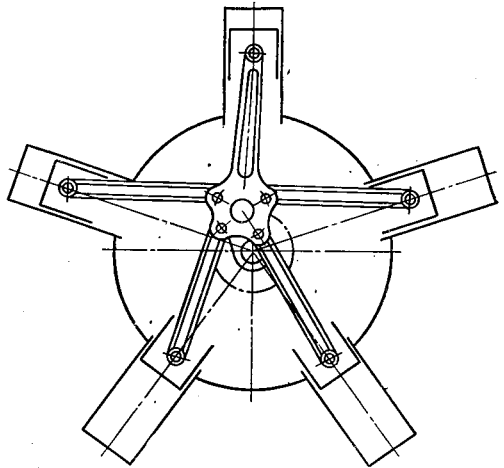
Схема двигателя с звездообразным расположением цилиндров
